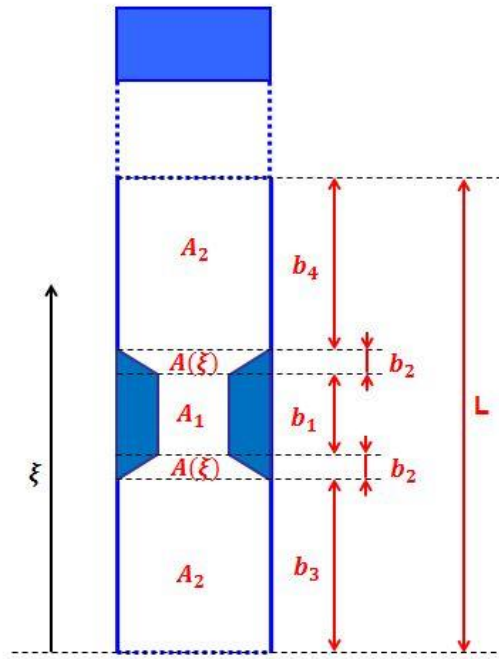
Dimensiones y posición del estrechamiento del tubo
